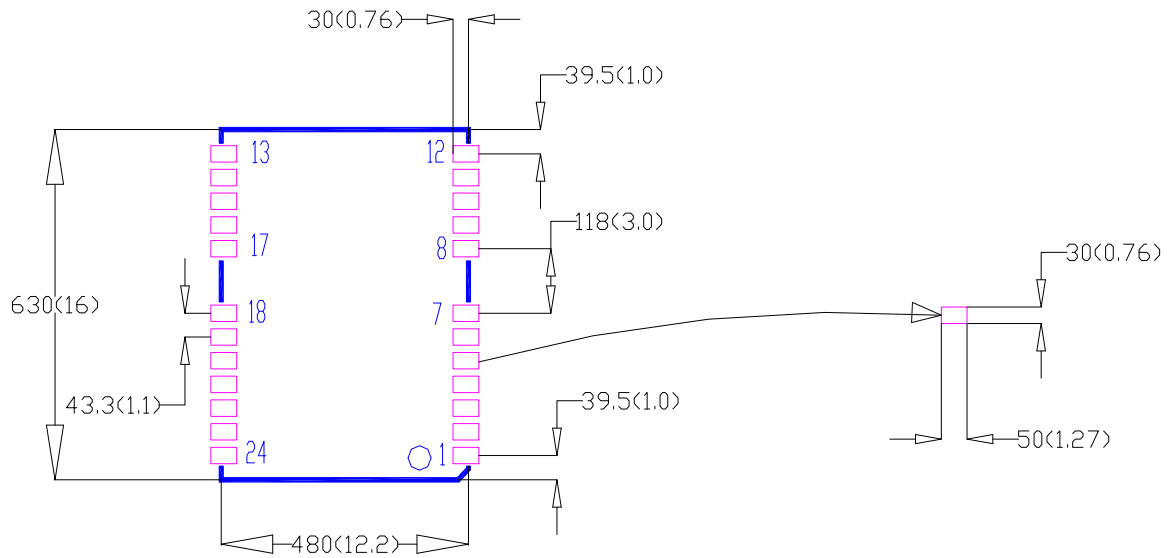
UM220-INS 系列模块推荐 PCB 封装设计 (尺寸单位: mil, 括号内单位: mm)
